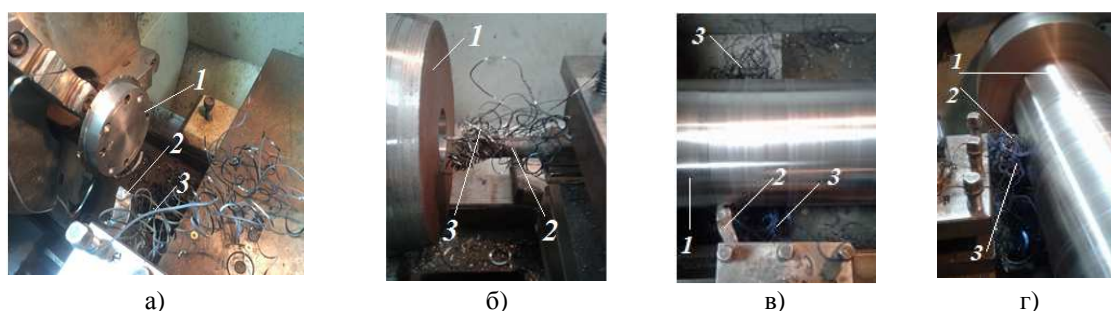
Процессы стружкообразования при токарной обработке: а – точение наружной цилиндрической поверхности; б – точение отверстия; в, г – точение вала; 1 – обрабатываемая заготовка; 2 – резец; 3 – стружки
